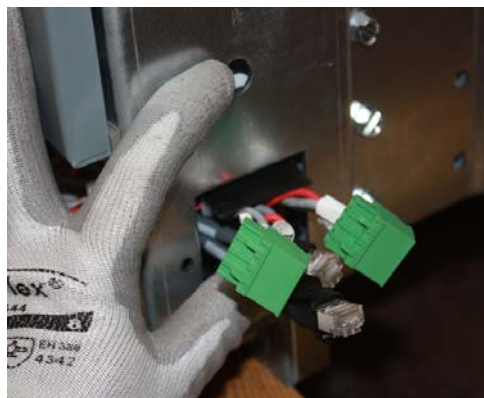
Cables ULP dirigidos y conectados a los puertos ULP etiquetados en el ducto para cables de la sección adyacente
